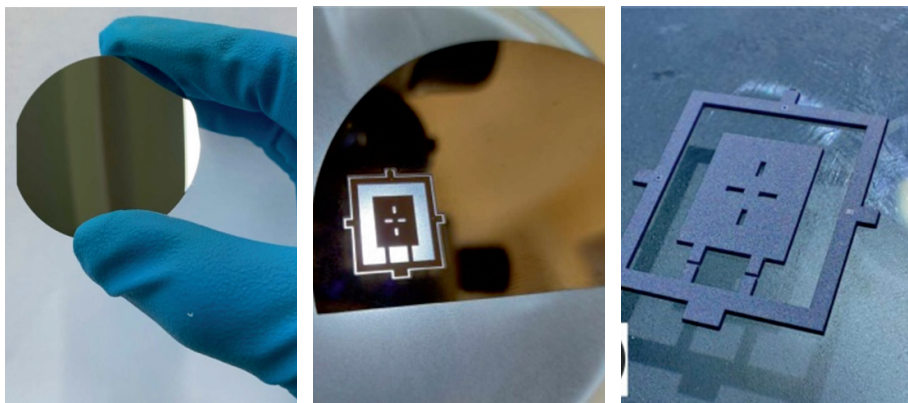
Заготовка и результат обработки образца из кристаллического кремния
